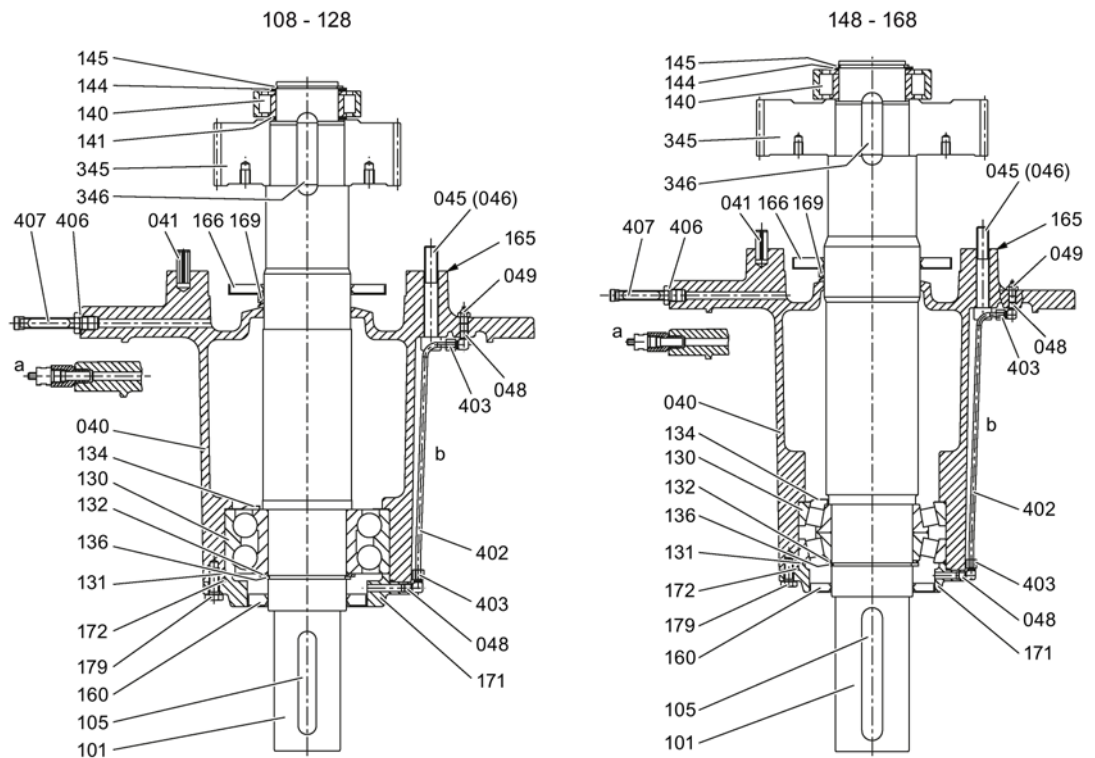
Rührwerksflansch Baugrößen 108 - 168
